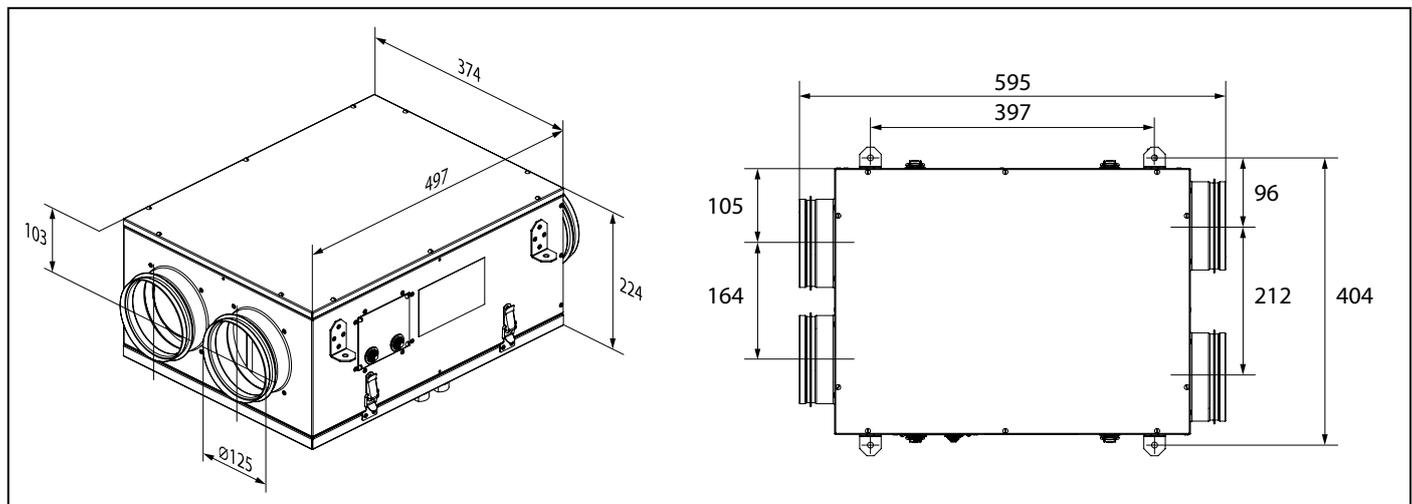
Габаритные размеры KOMFORT Ultra D105-A
